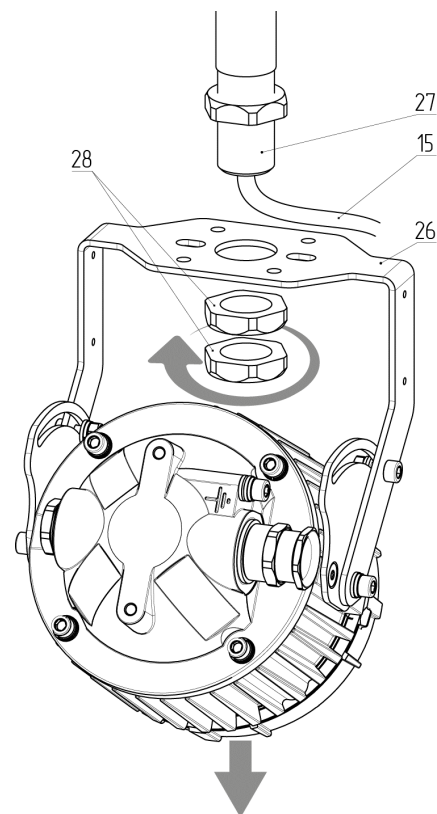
Демонтаж светильника с креплением ТМ21/22
